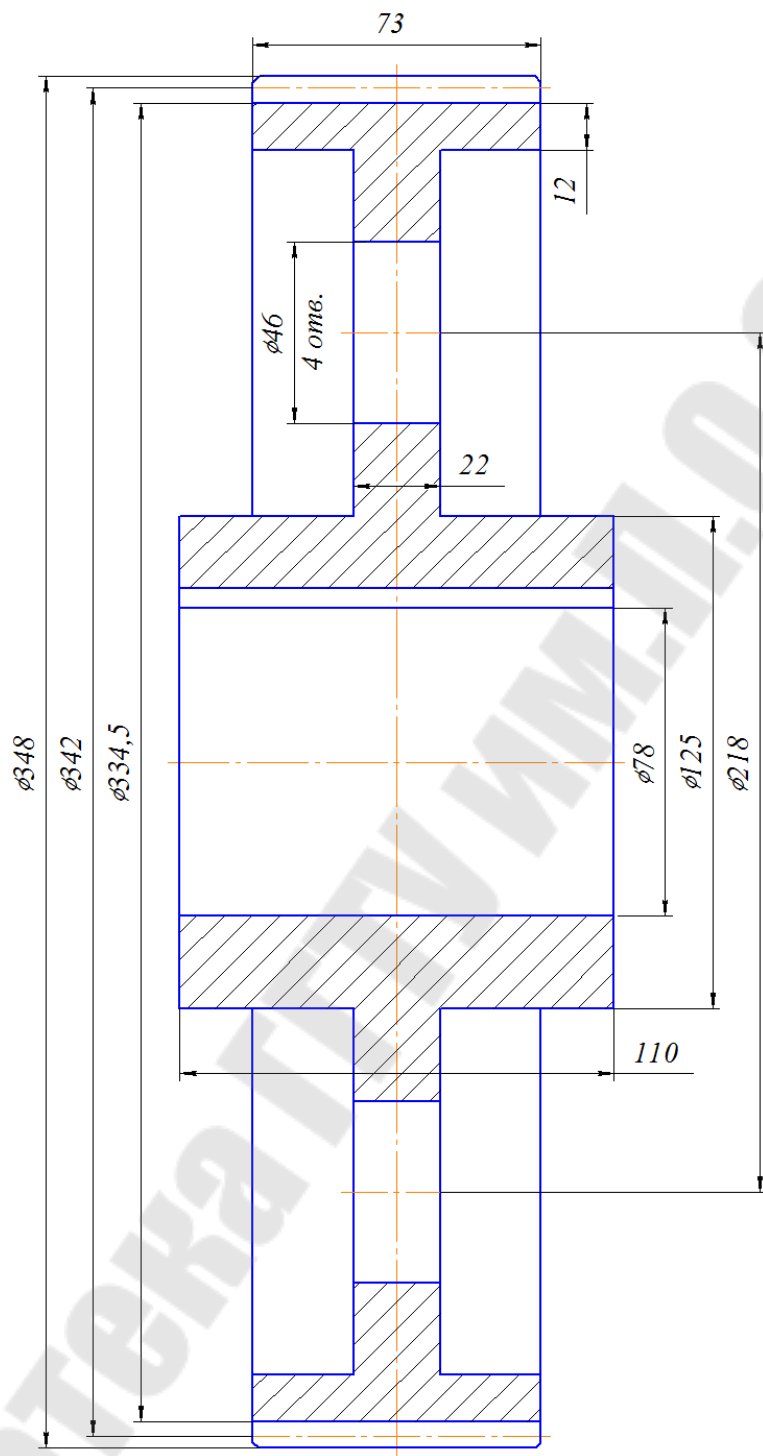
Эскиз зубчатого колеса тихоходной ступени редуктора
